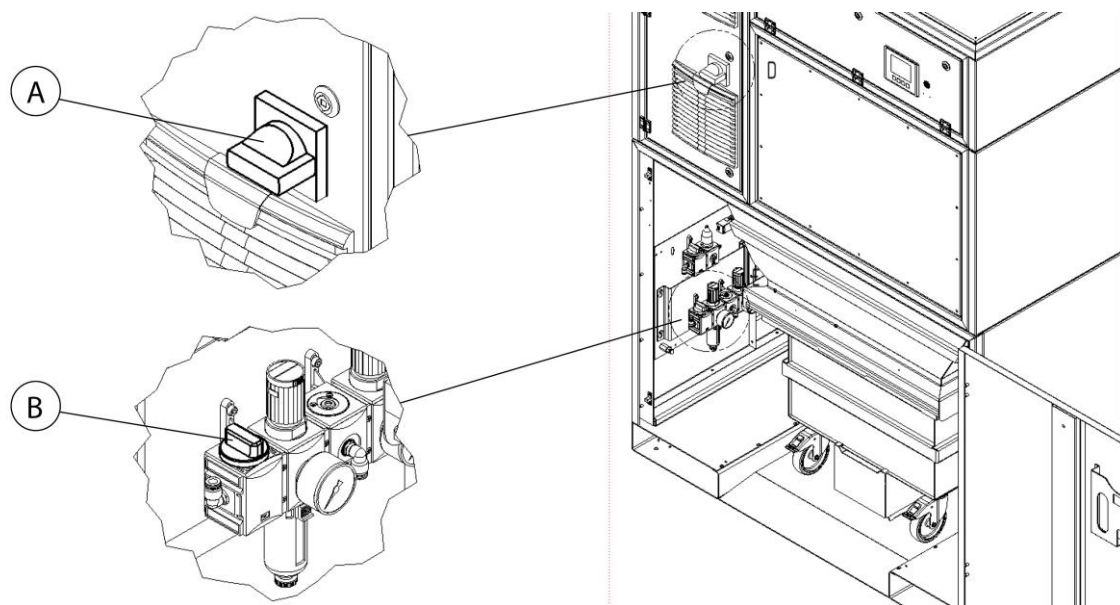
Scollegare il prodotto dalla rete di alimentazione e dalla rete di aria compressa
